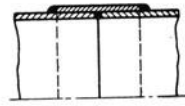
Schweißnahtsicherung mittels Überschieber.
